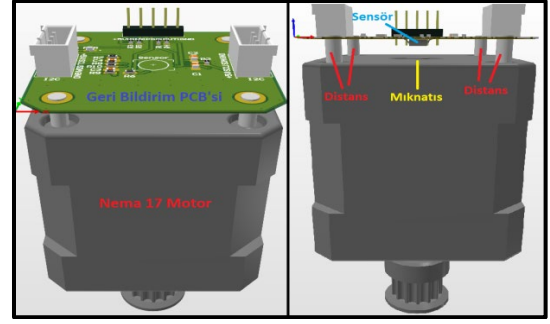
Geri bildirim sistemi PCB tasarımı görüntüsü.
